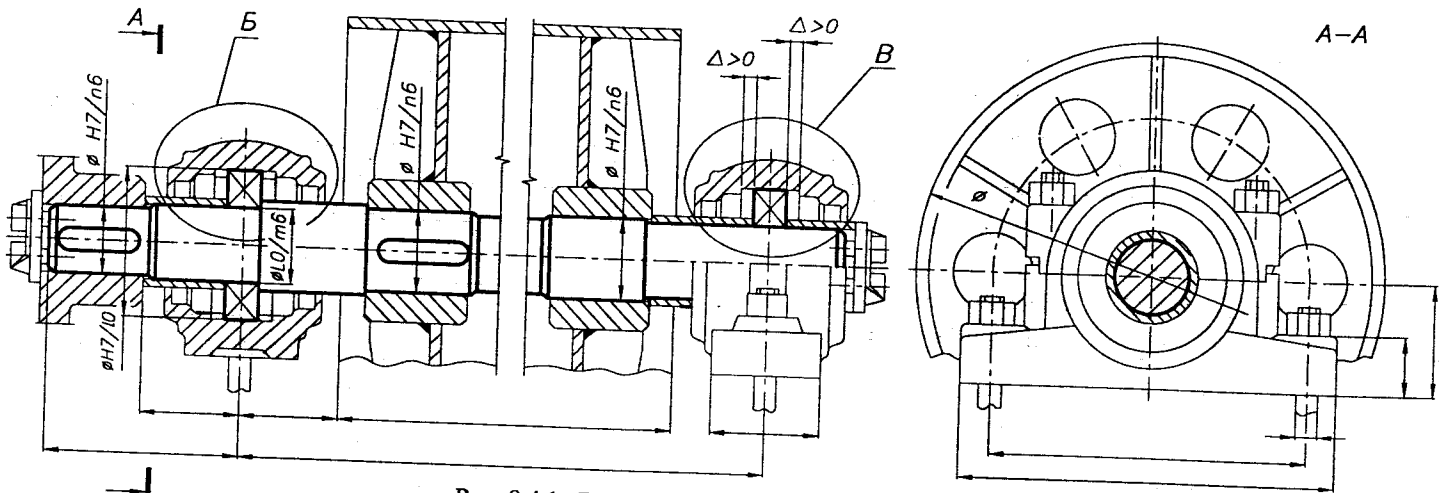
Подшипниковые узлы приводного вала барабана
